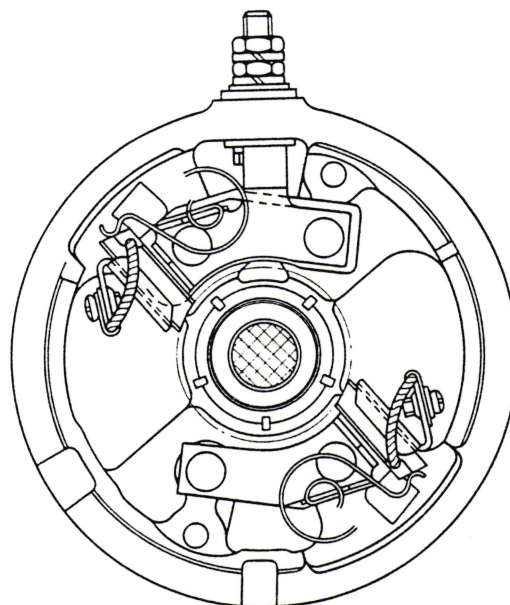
Querschnitt der Lichtmaschine durch die Ankerwelle mit Ansicht auf das Kollektorlager.
